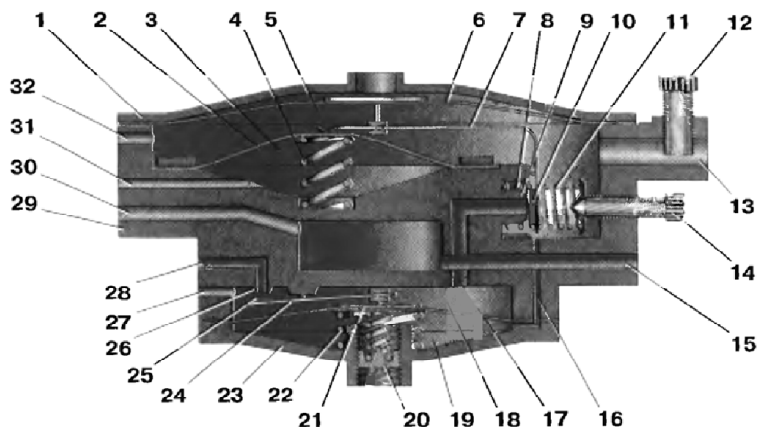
Рычажно-мембранный редуктор-испаритель «САГА-6»:
